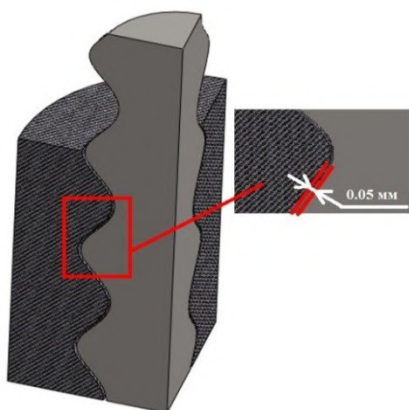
3D- CAD-модель з'єднання в графічному редакторі SOLIDWORKS
